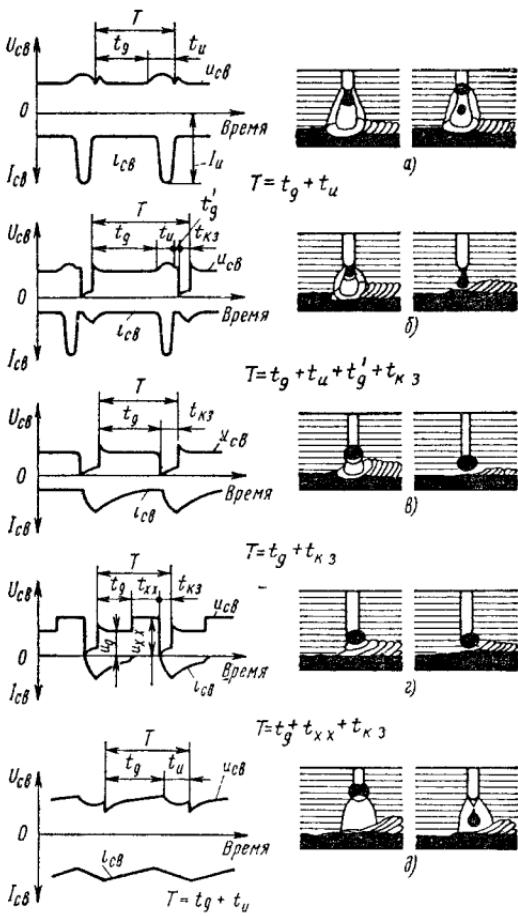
Внешний вид разрядного промежутка и осциллограммы напряжения и тока сварки:
